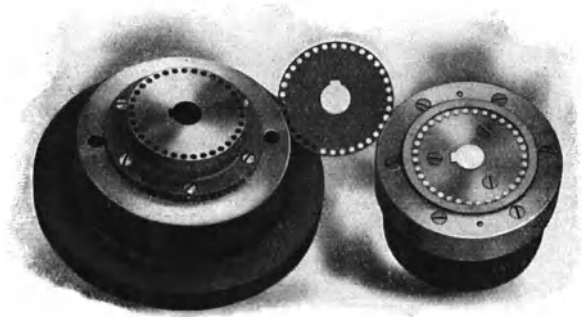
Ansicht des Werkzeuges in Abb. 204.
